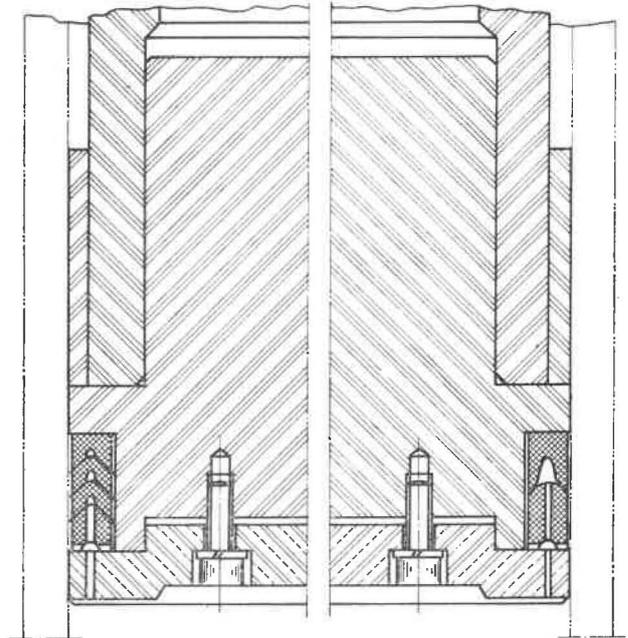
Détail du montage des joints chevron ou des joints à lèvres destinés à remplacer les joints toriques des étançons.
